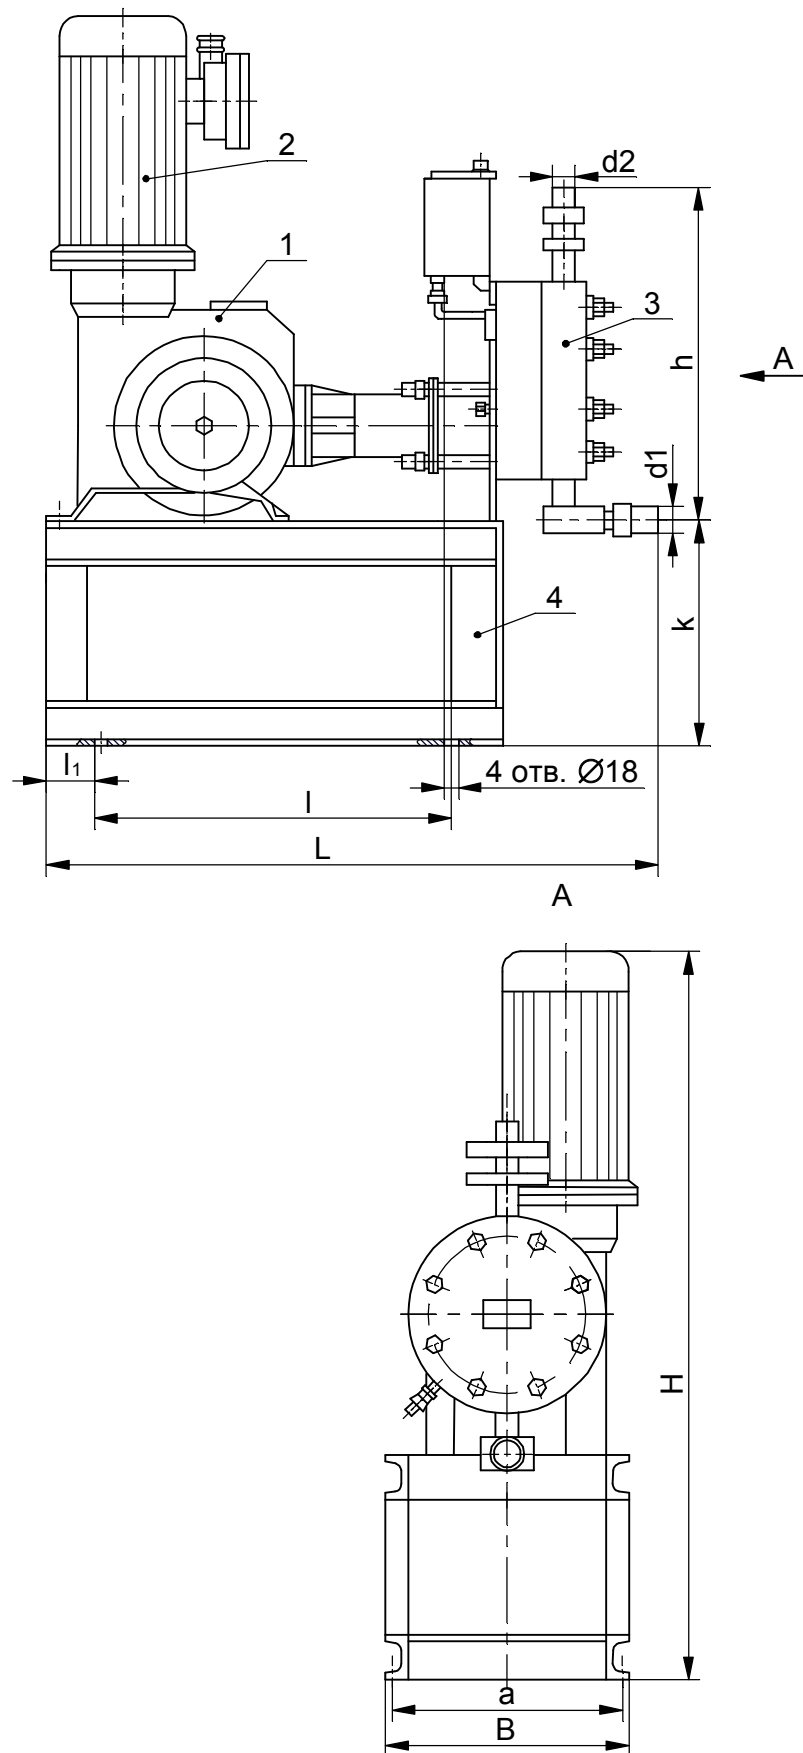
Внешний вид агрегата с параметрами номинального режима 400/16; 400/40; и 630/25. Габаритные и установочные размеры
